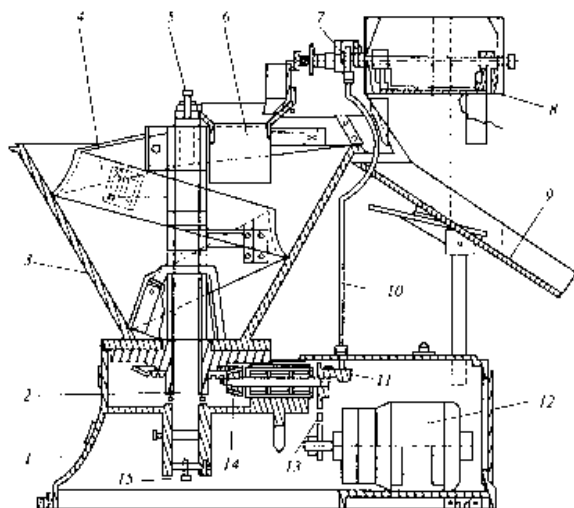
Конструктивная схема тестоокруглительной машины: 1 - станина; 2- стойка; 3 - чаша; 4- спиральный желоб; 5, 15 - винты; 6- приемная воронка; 7 - кривошип; 8 - мукопосыпатель; 9 - наклонный спуск; 10 - тяга; 11 - палец звездочки; 12 - электродвигатель; 13 - цепная передача; 14 - зубчатая передача
